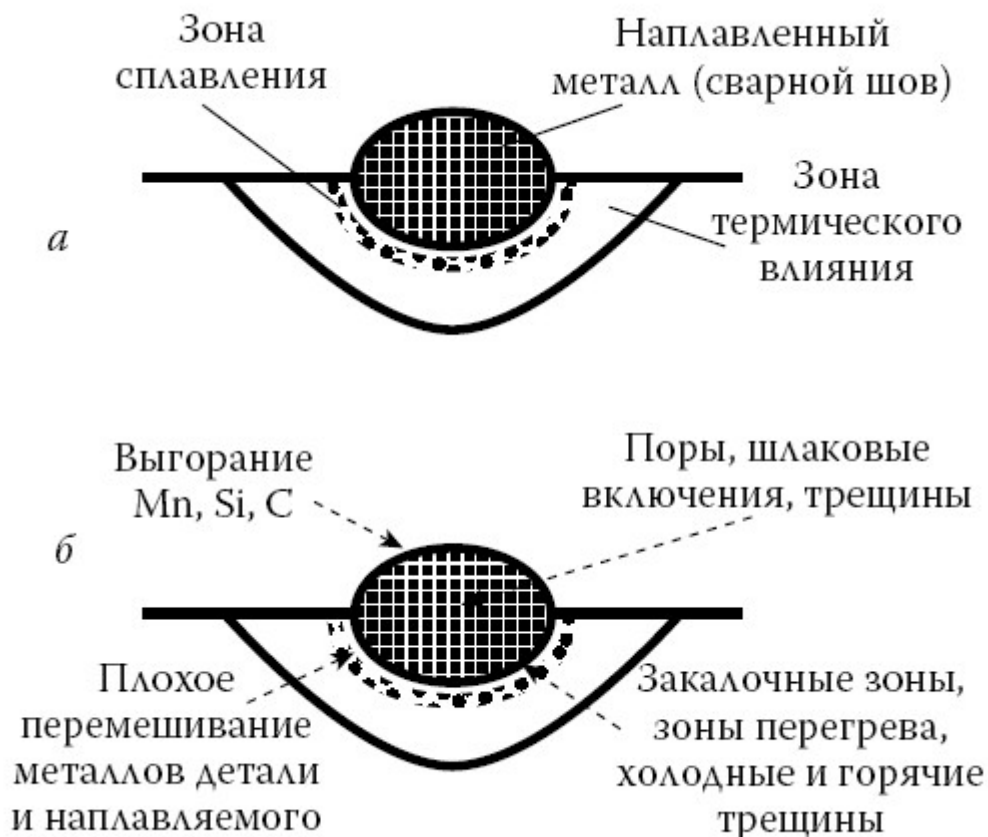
Зоны сварного шва (а) и возможные дефекты в нем (б)
